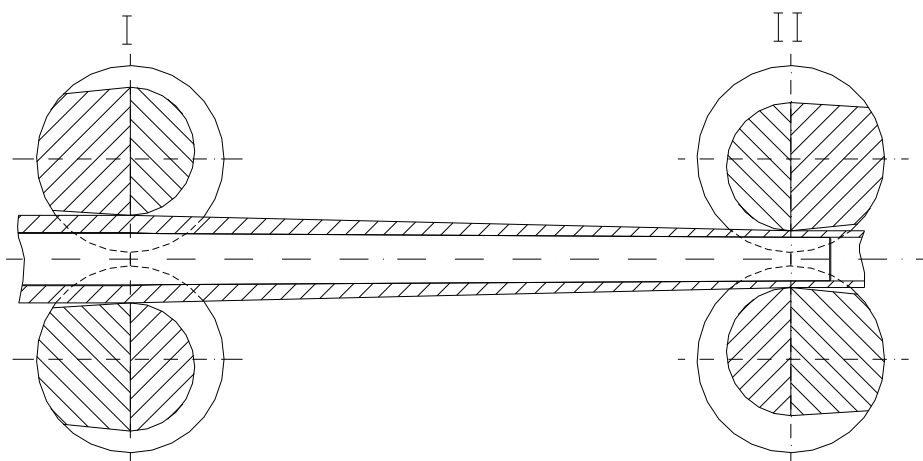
Схема прокатки труб на стане ХПТ:
